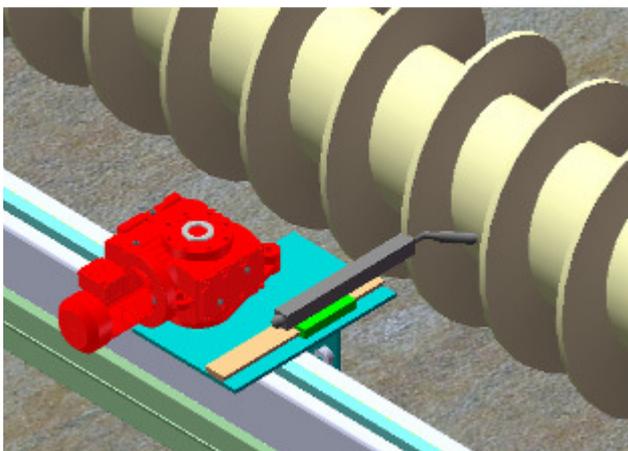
Desenho com detalhe do rasgo no flange
